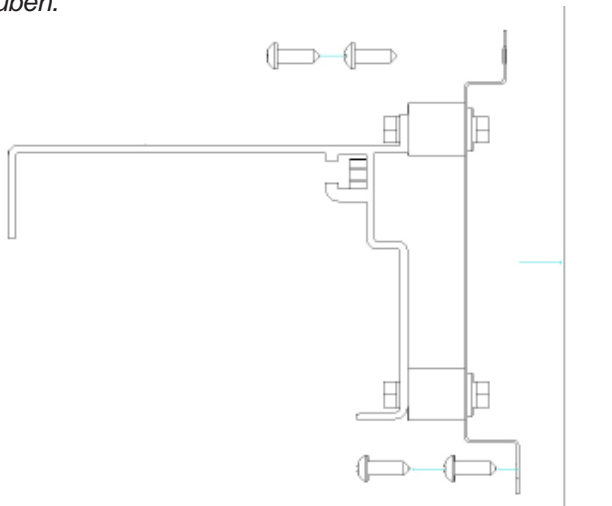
Fixierung des Heizgerätes mit 2 M8 Fächerscheiben und M8x140 Befestigungsbolzen.
